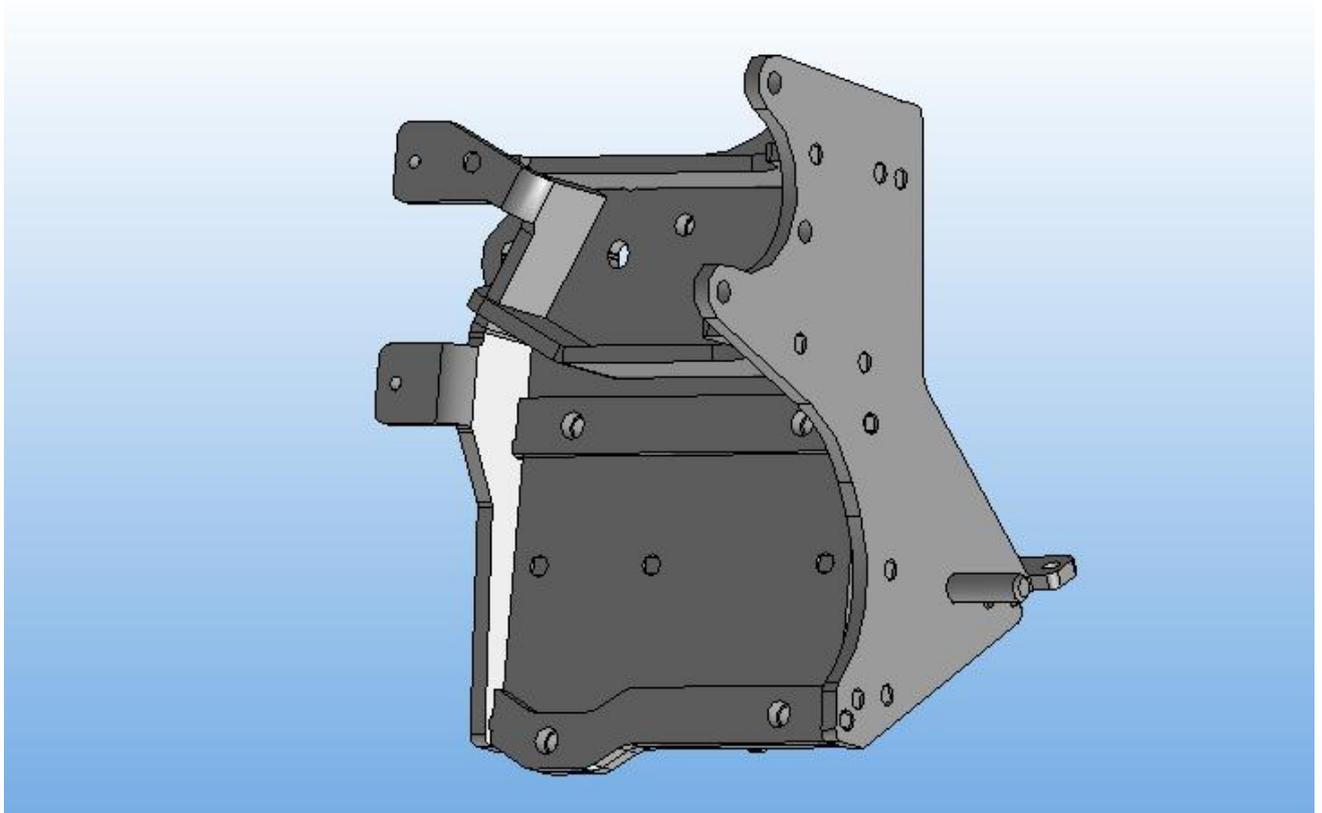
Корпус кронштейна навесного оборудования двигателя
